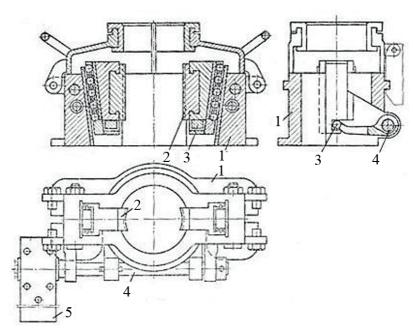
Универсальный трубодержатель: 1 – корпус; 2 – две съемные плашки с насечками; 3 – два кулачка; 4 – валик; 5 – ножная педаль
